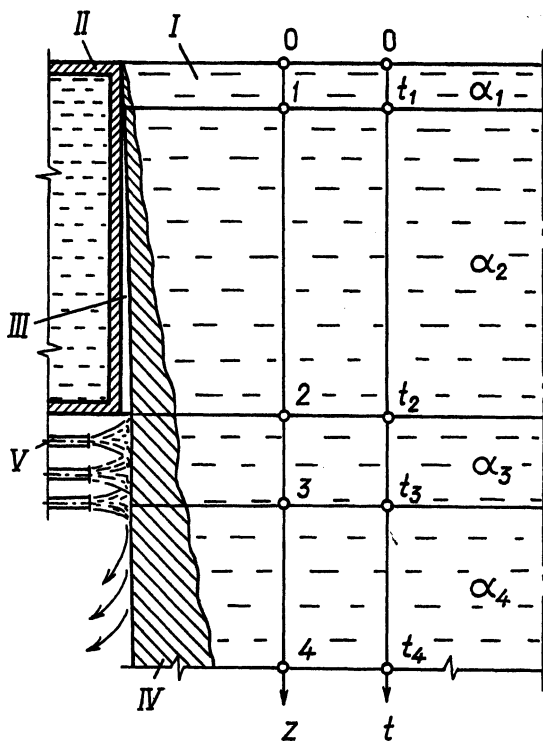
Расположение расчетных зон в пределах кристаллизатора и первой зоны форсуночного охлаждения: I – расплав металла; II – стенка кристаллизатора; III – газоздушный зазор; IV – твердая корка литой заготовки; V – форсунки водяного охлаждения
